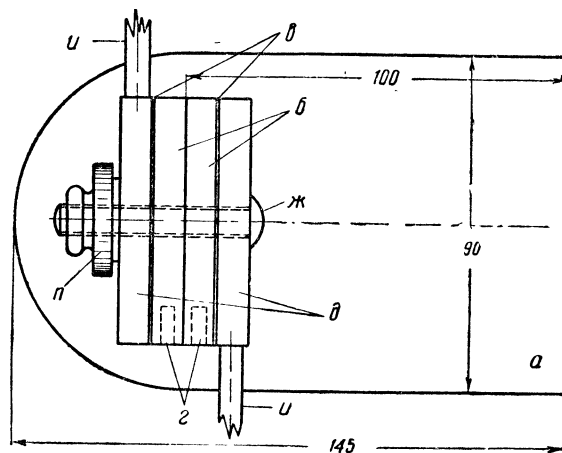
Сборочный чертеж антенны (вид сверху): *а* — основание; *б* — стойки; *в* — контактные кольца; *г* — гнезда; *д* — диски для крепления лучей антенны; *ж* — стяжной болт; *и* — внешние трубки лучей; *п* — фигурная гайка
